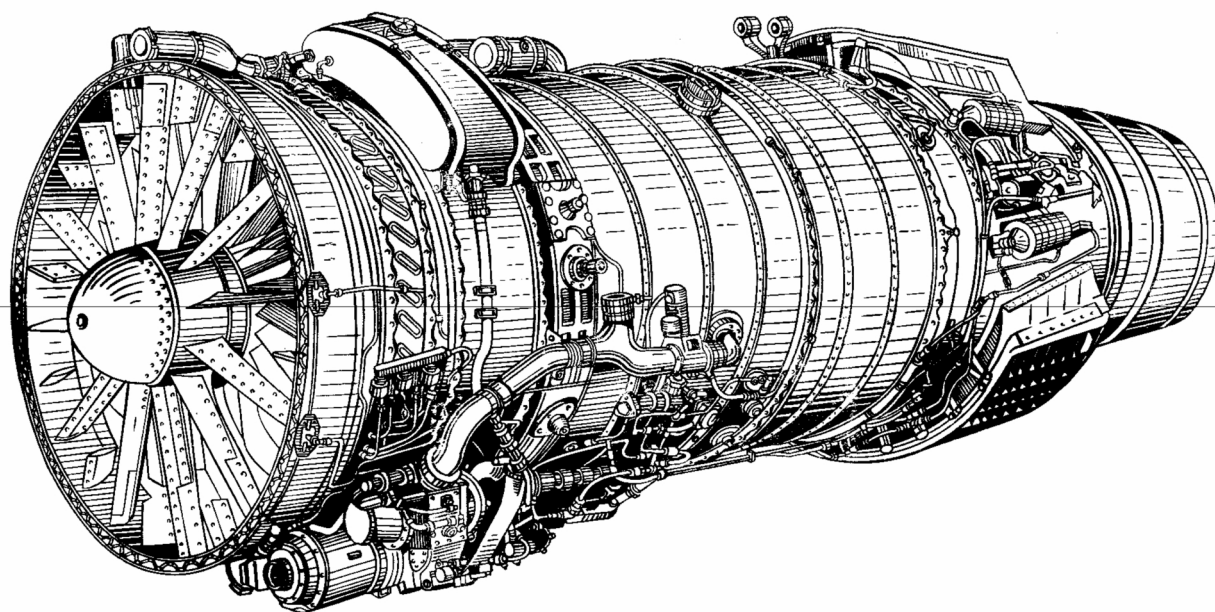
Двигатель НК-8-2У с реверсом (вид слева)
